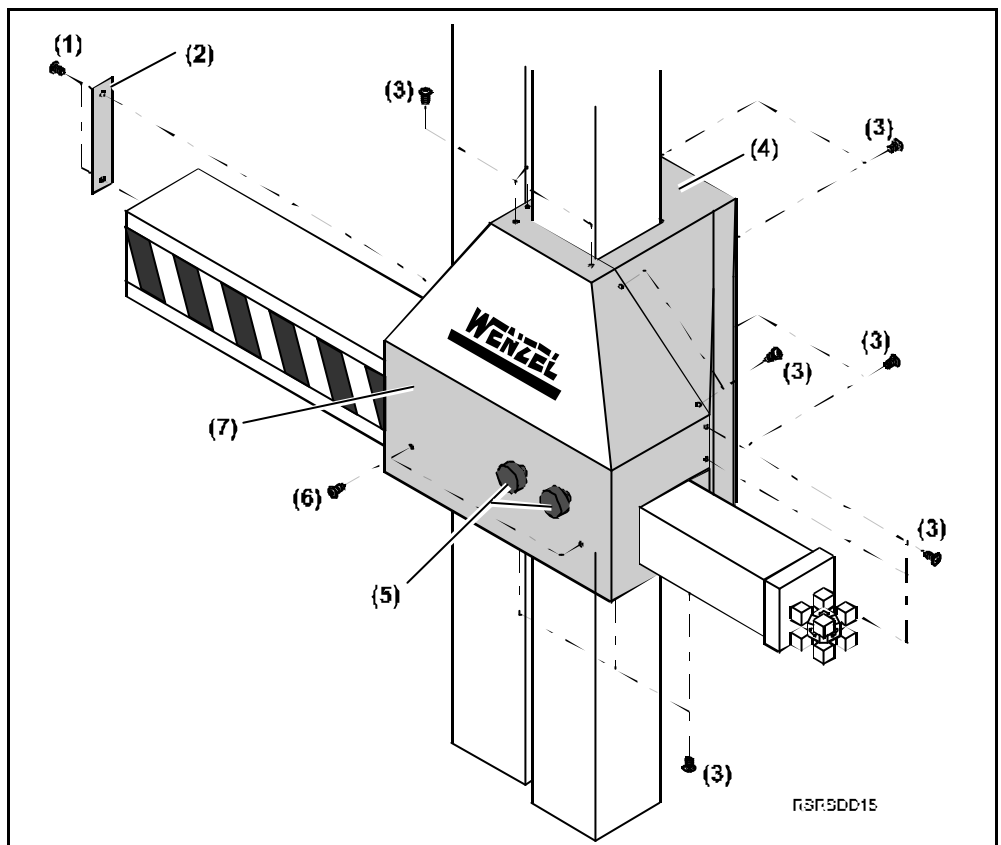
Schutzabdeckung (Schutzhaube) mit Befestigungsschrauben
